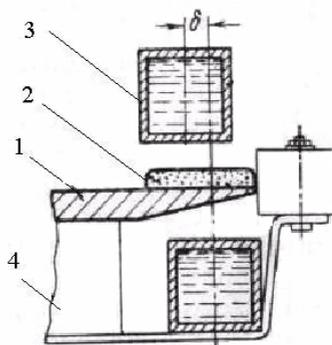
Схема расположения наплавляемой детали в индукторе:
